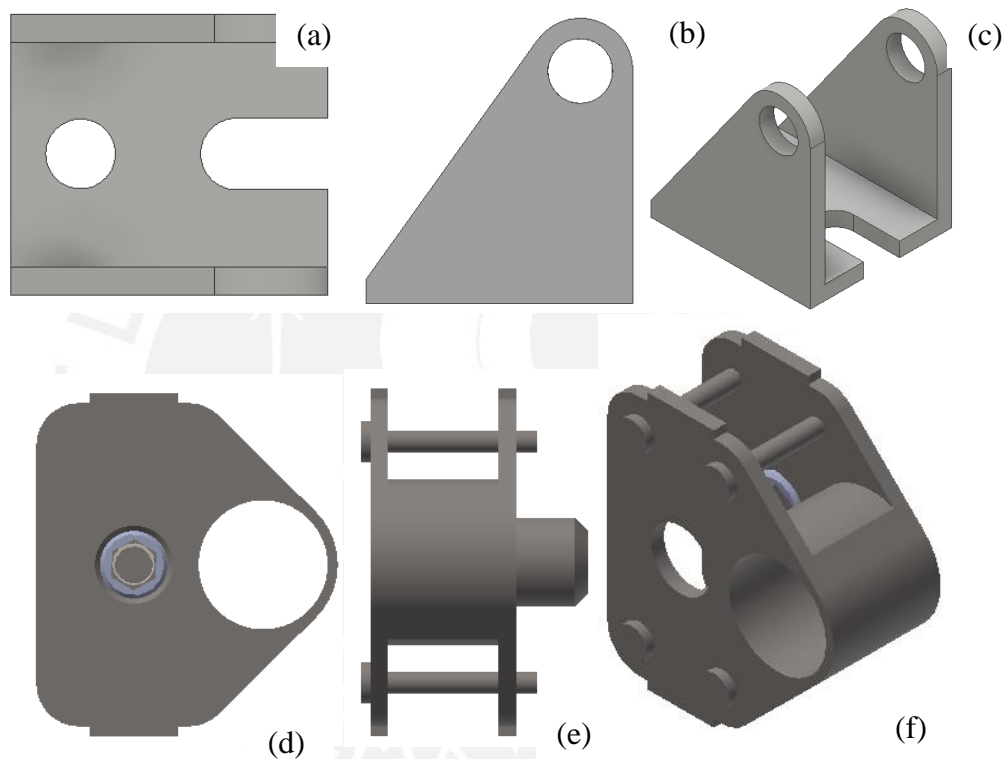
Soporte de unión actuador lineal giro asiento/asiento Vistas Superior(a) Lateral (b) Isométrica(c),
